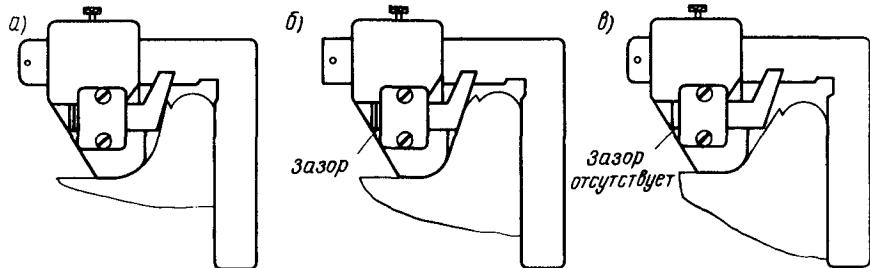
Положения специального шаблона для браковки колес по остроконечному накату гребня, показывающие что колесная пара
